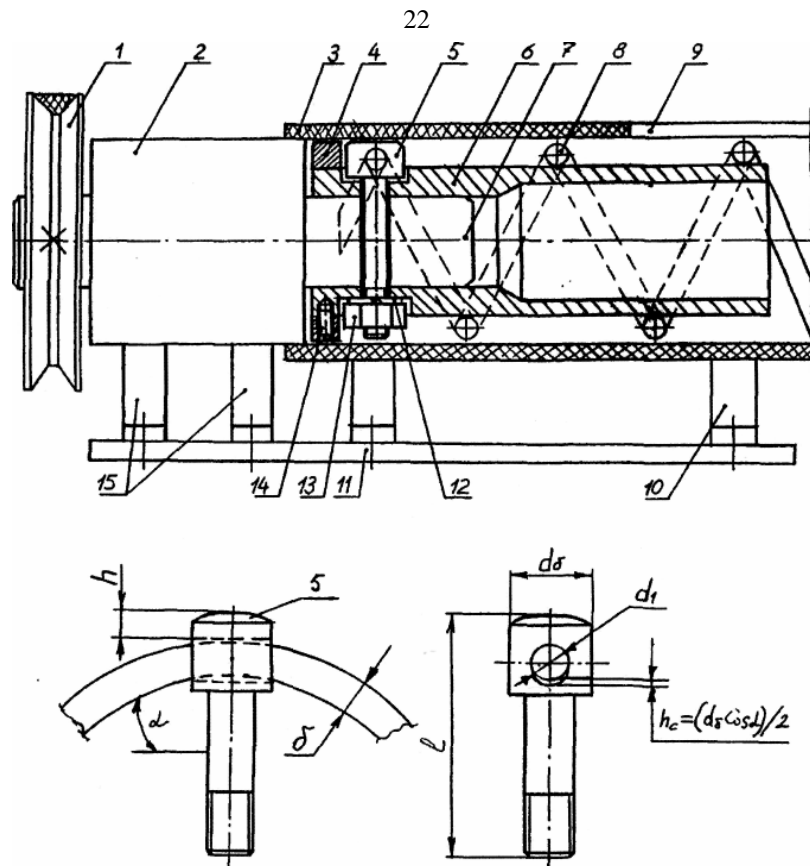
Универсальный вариант устройства для привода длиномерной вращающейся пружины:
